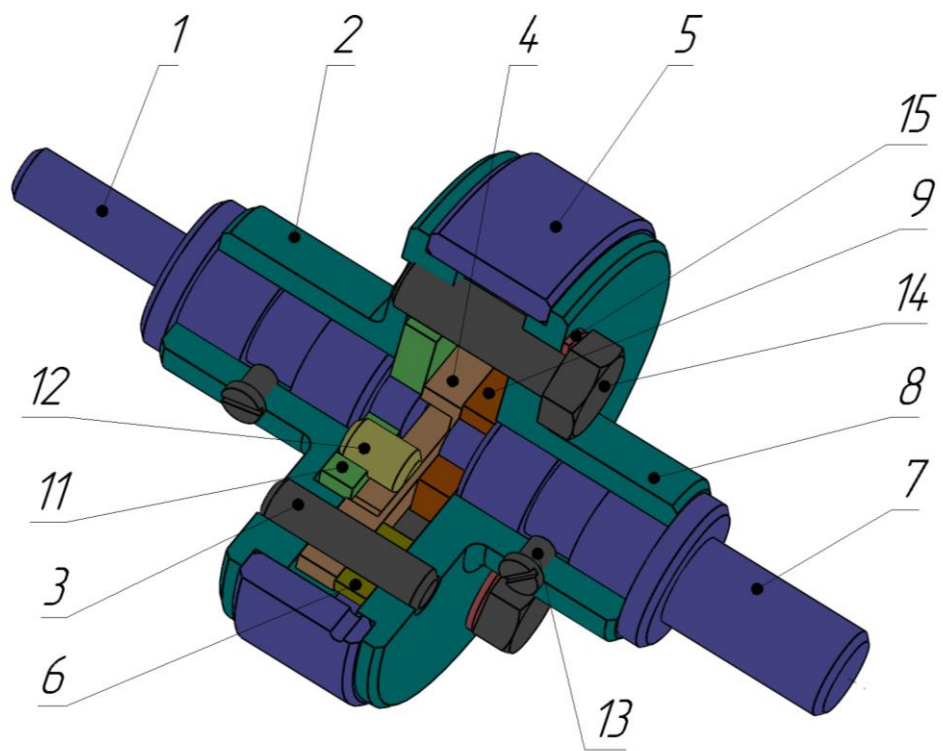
Сборка кривошипно-кулисного механизма – разрез 1
